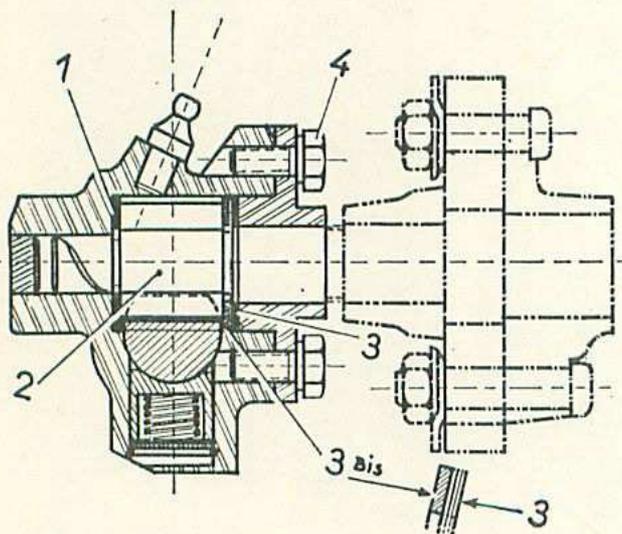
Vue en coupe du boîtier de crémaillère.
